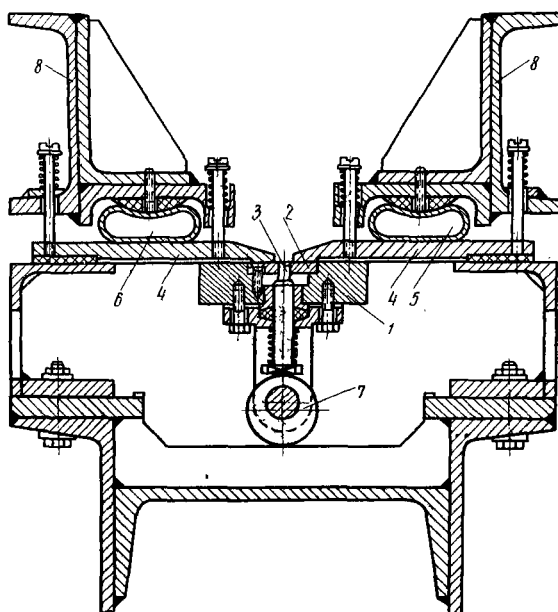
Приспособление пневмошлайфового типа для сварки прямолинейных швов
